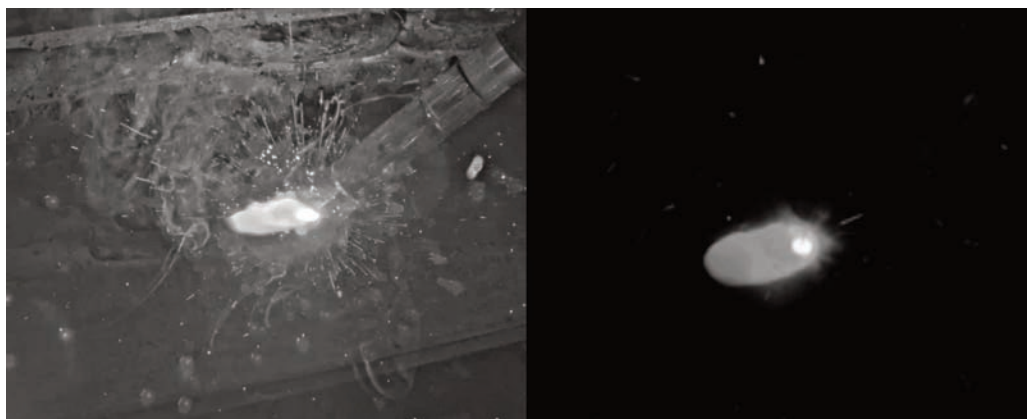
| Ansicht des Schweißers mit (l.) und ohne (r.) den 3D-Schweißhelm.
